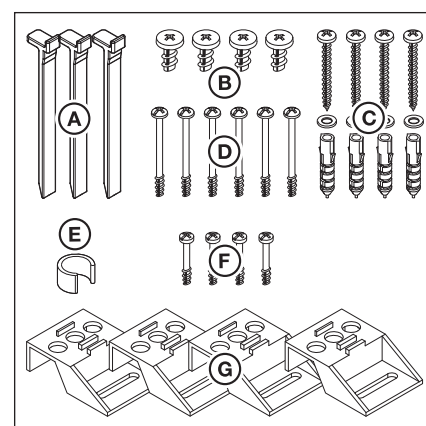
Пакет со вспомогательными принадлежностями для корпуса блока управления
